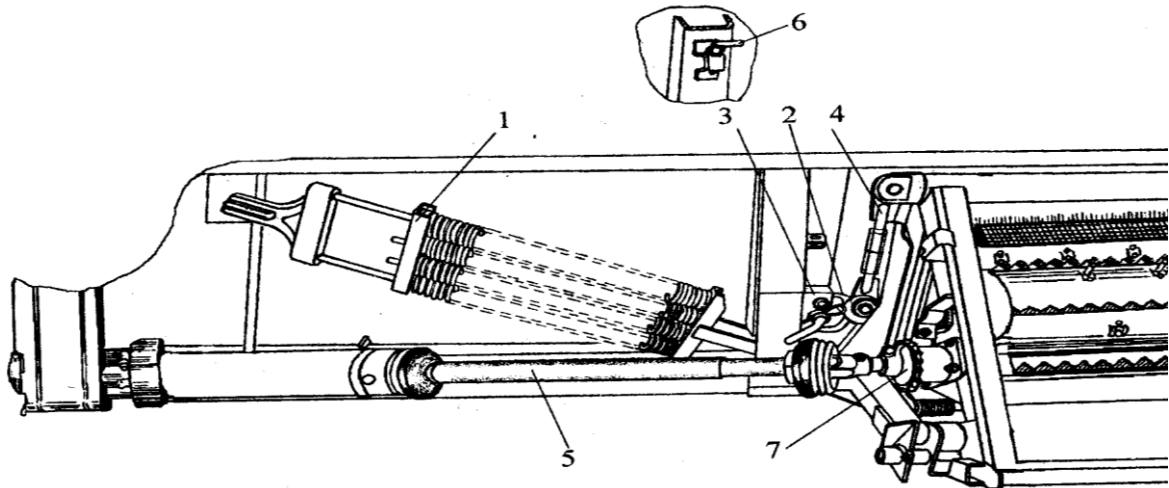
Уравновешивающий механизм жатки (левый): 1 – блок пружин; 2 – рычаг; 3 – кронштейн; 4 – подвеска регулируемая; 5 – вал карданный; 6 – рукоятка; 7 – контрпривод
